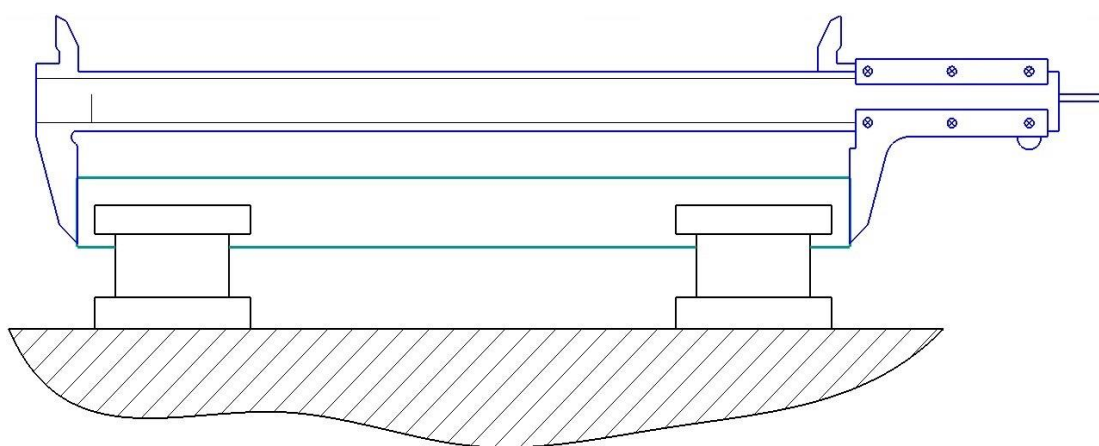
Схема проведения замеров длины трубной заготовки
